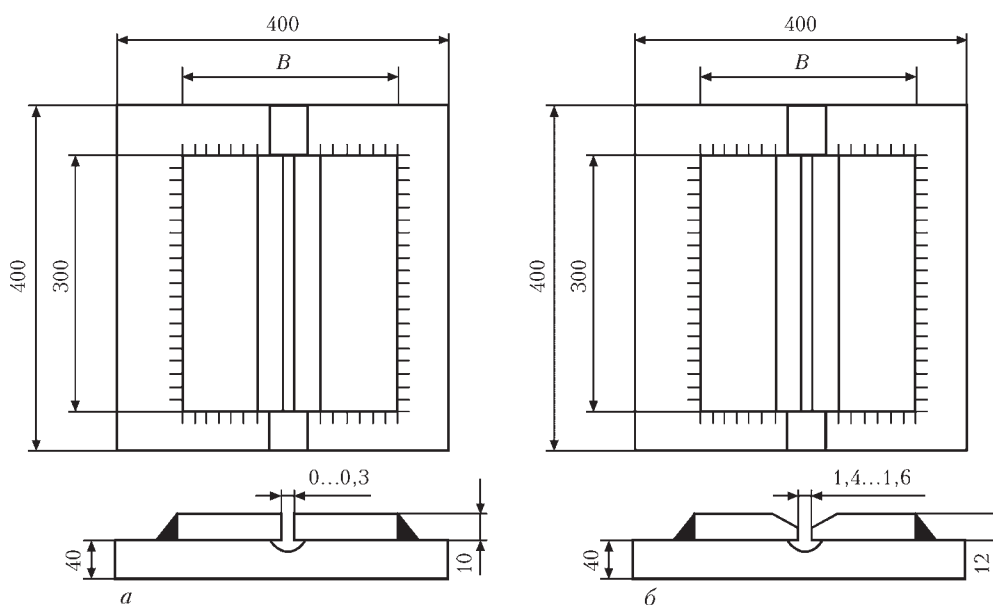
Технологическая проба с регулируемой жесткостью для гибридной и лазерной (а) и дуговой сварки (б)
